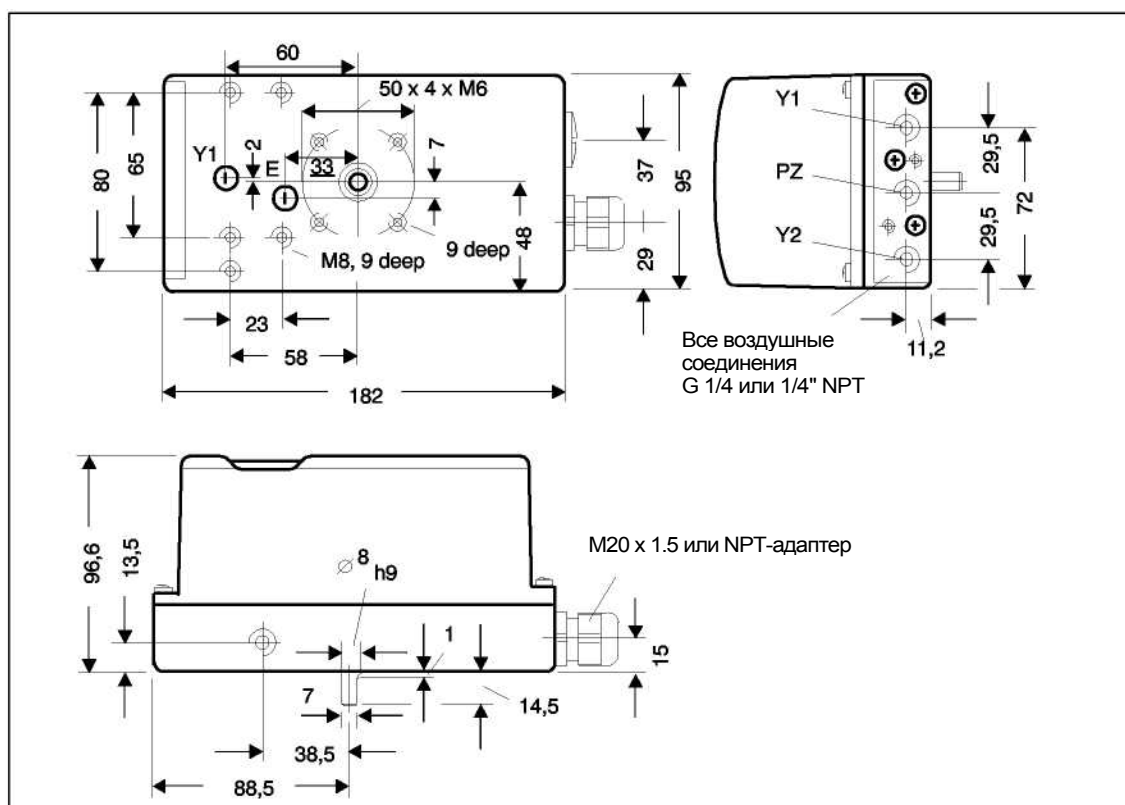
Размерный чертеж версии в пластиковом корпусе 6DR5xx0
